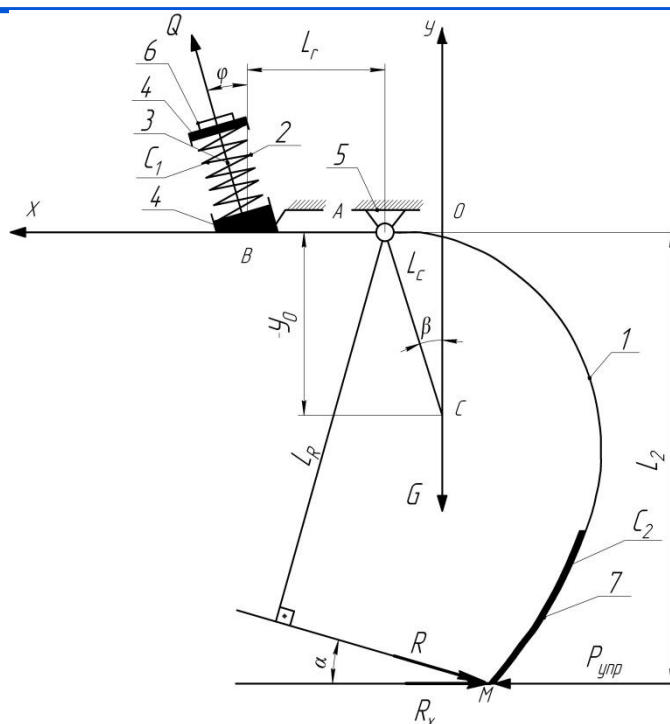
Схема конструкции стойки чизель – культиватора с шарнирно-упругим креплением к раме 1 –стойка; 2- цилиндрическая пружина; 3 – хомут; 4 – верхние и нижние стаканы; 5 – рама; 6 – гайка; 7 – лапа.
